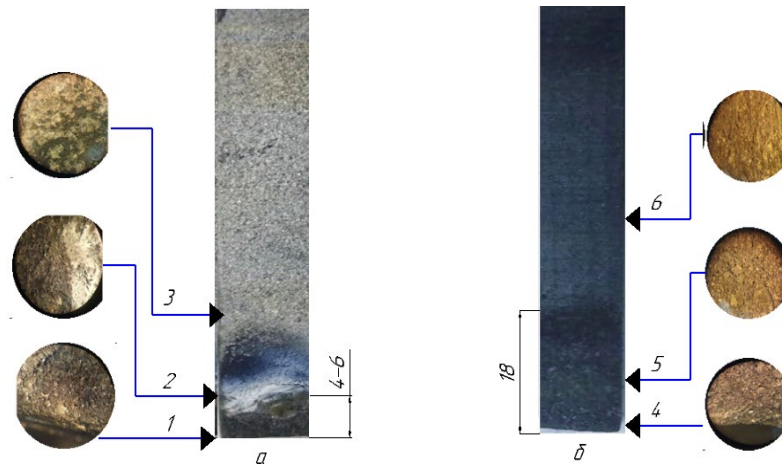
Зовнішній вигляд графітової пластини після зварювання а – з боку покриття; б – зі зворотнього боку
